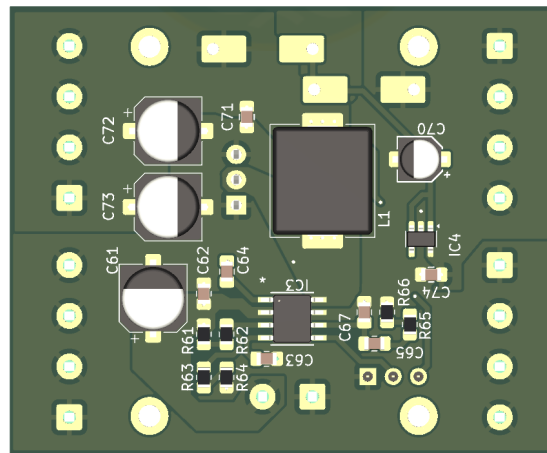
PCB líneas 3,3[V] y 5[V].
